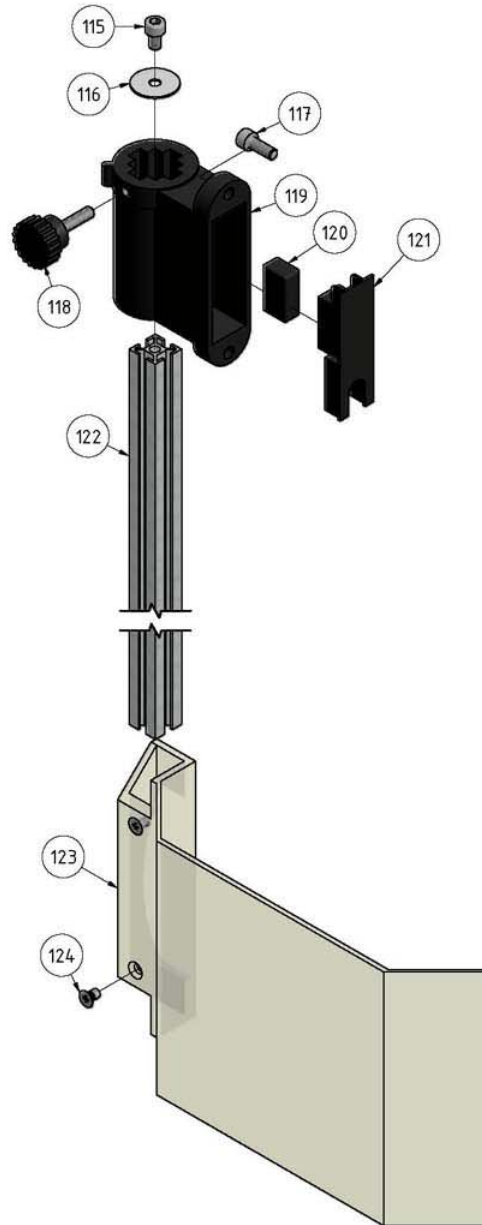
Fräsfutterschutz - Milling chuck protection
